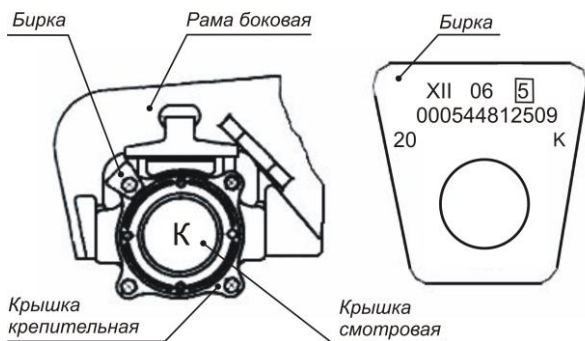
Внешние отличительные признаки буксового узла с коническим подшипником в габаритных размерах 130×250×160 мм торговой марки SKF
